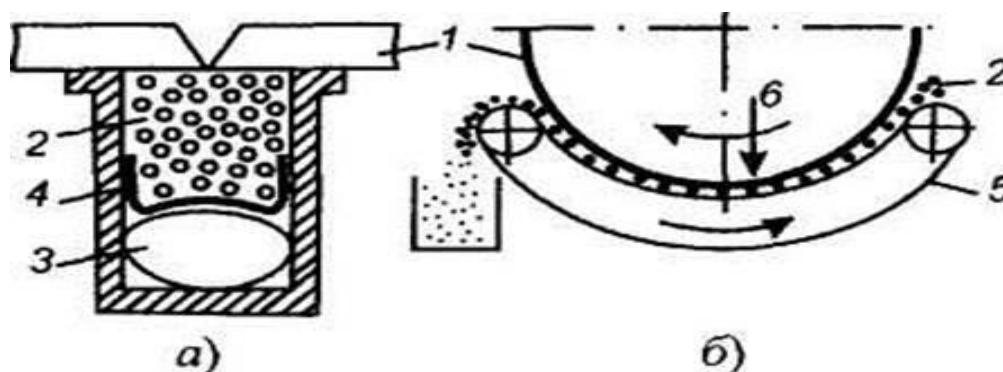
Сварка на флюсовой подушке: а – плоских конструкций; б – внутренних кольцевых швов (стрелками указаны направления перемещений); 1 – изделие; 2 – флюс; 3 – воздушный шланг; 4 – лоток; 5 – профилированная гибкая лента, 6 – электрод
